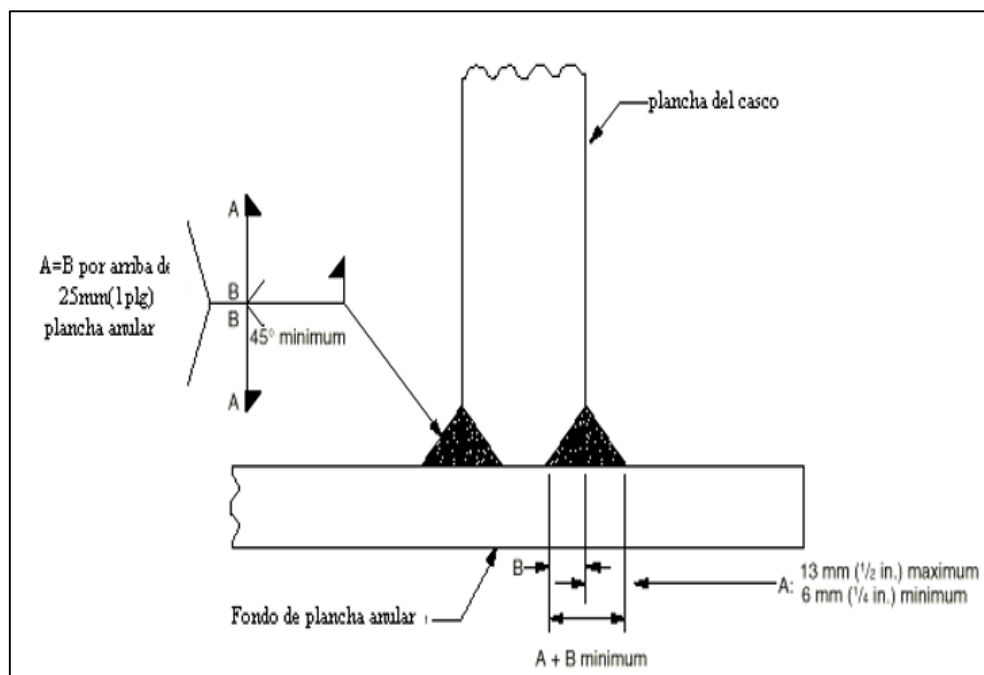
Detalle soldadura ranura-filete doble para planchas de fondo con un espesor nominal mayor que 13mm (1/2 plg)
